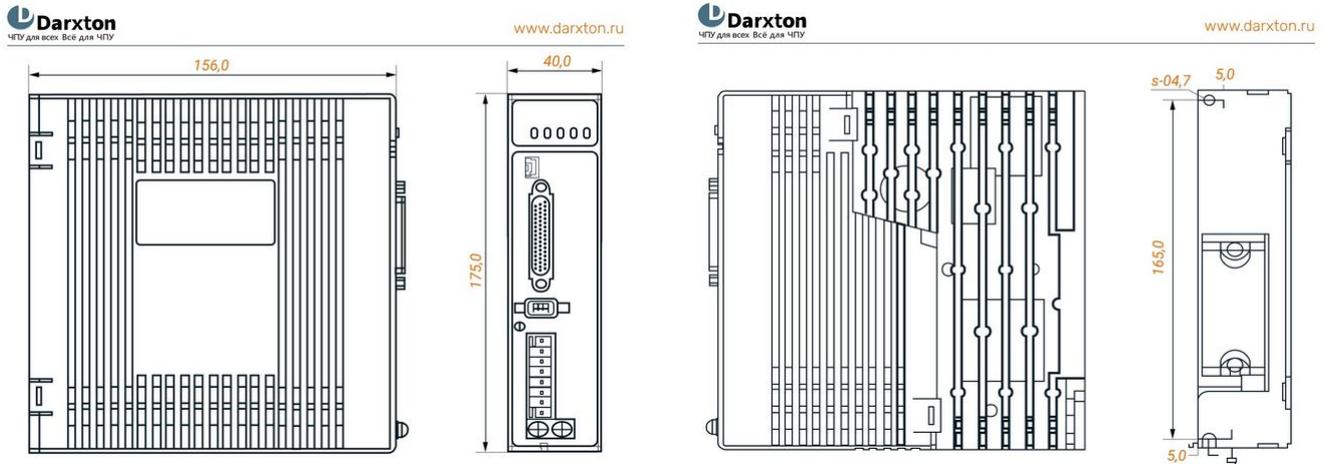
Габаритные размеры драйвера ELP-RS400Z
